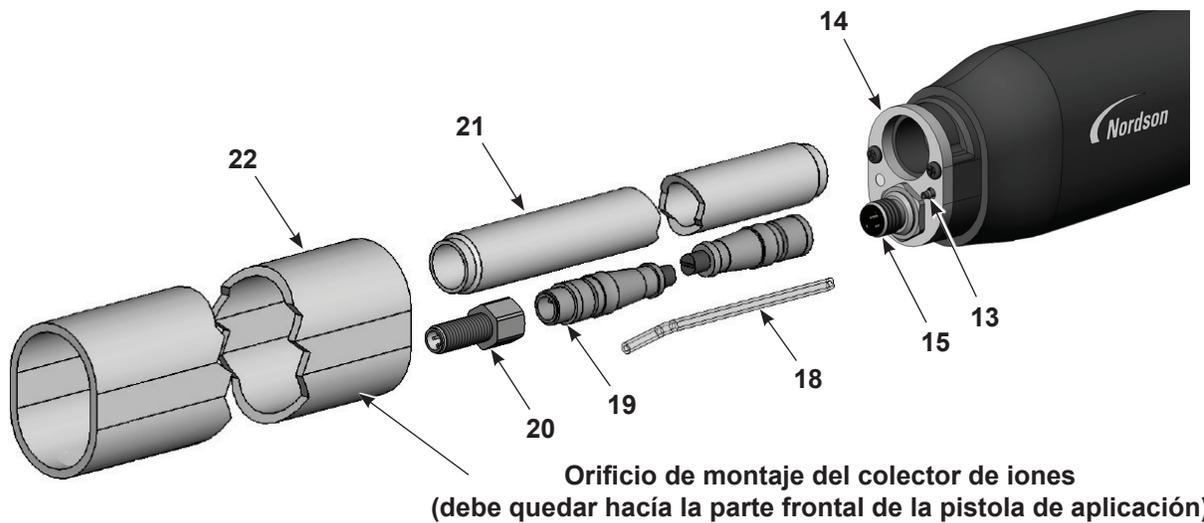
Desmontaje de una pistola de montaje en tubo 2 de 5
